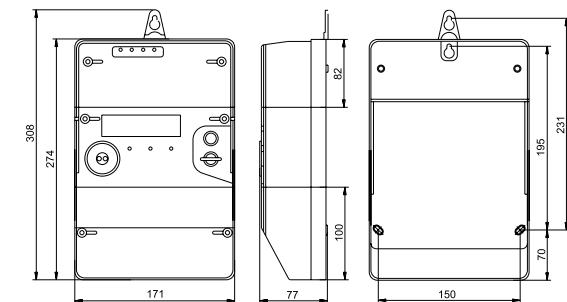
Габаритные и присоединительные размеры счётчиков
